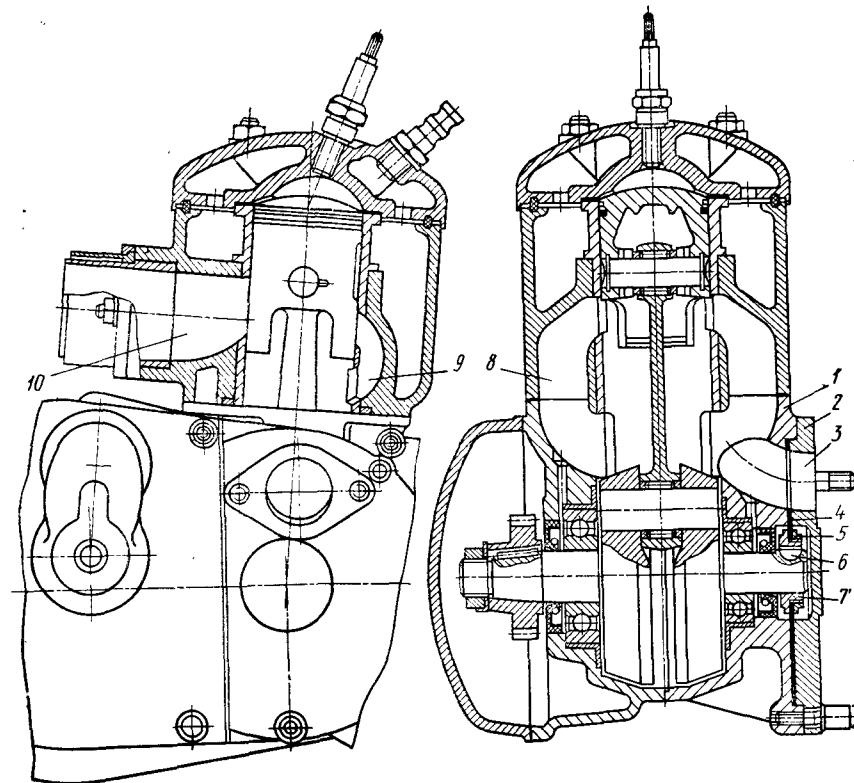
Двухтактный двигатель С2-125 с золотником на впуске:
